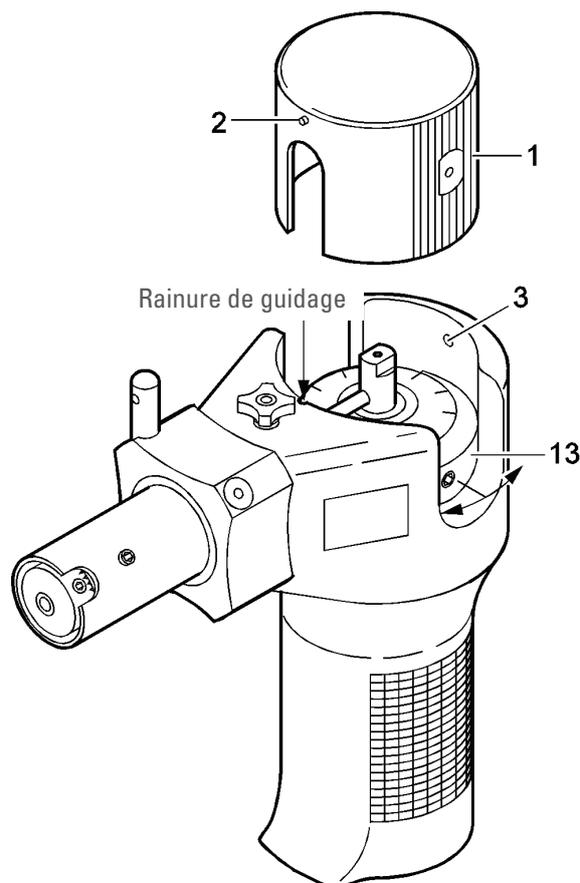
Dessin symbolique - Mise en service de la machine à limer à main
